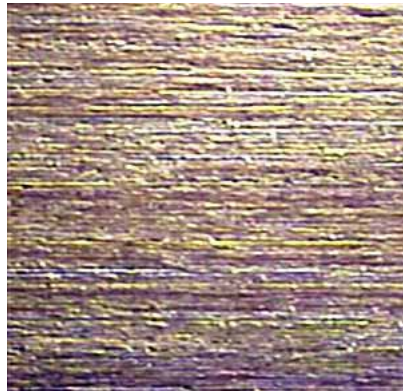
Detalle de superficie de frondosa trabajada con lija (aumento de lupa de 6,4, escala 1/2)
